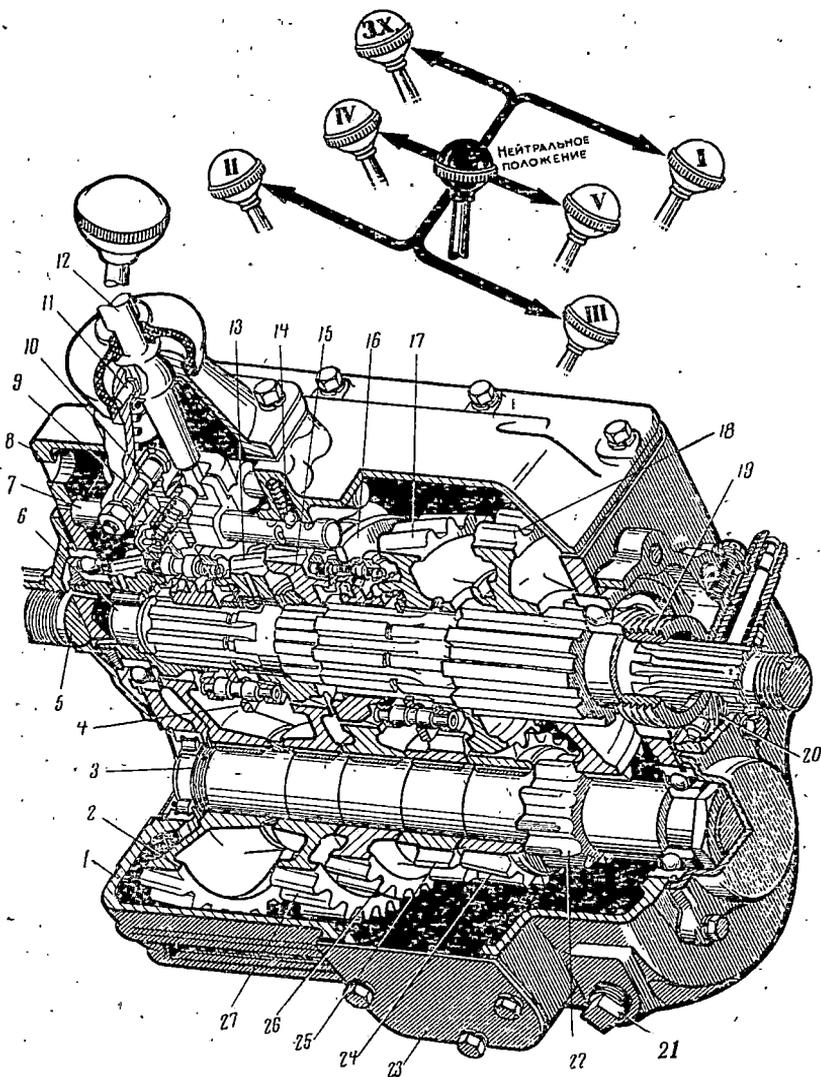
Коробка передач автомобиля ЗИЛ-164А (ЗИЛ-130):
